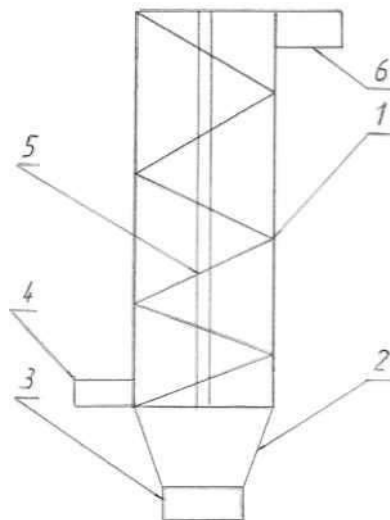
Принципова схема глушника [15]: 1 – корпус; 2 – конічна частина; 3 – оливозбірник; 4 – вхідний патрубок; 5 – гвинтова поверхня; 6 – вихідний патрубок.
